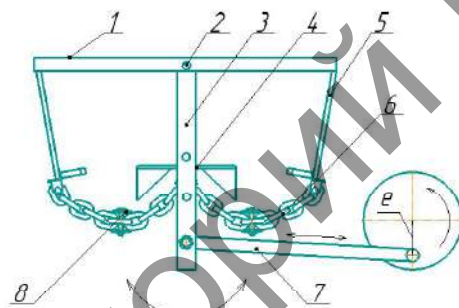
Схема рабочего оборудования цепного агрегата с волновой рабочей камерой
